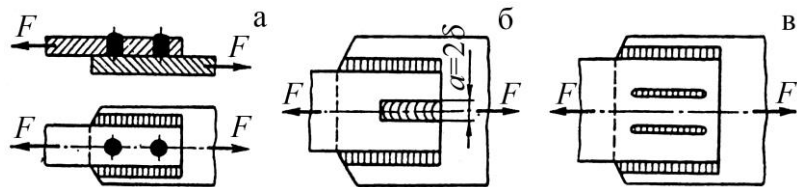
Коркові, прорізні та проплавні зварні шви
